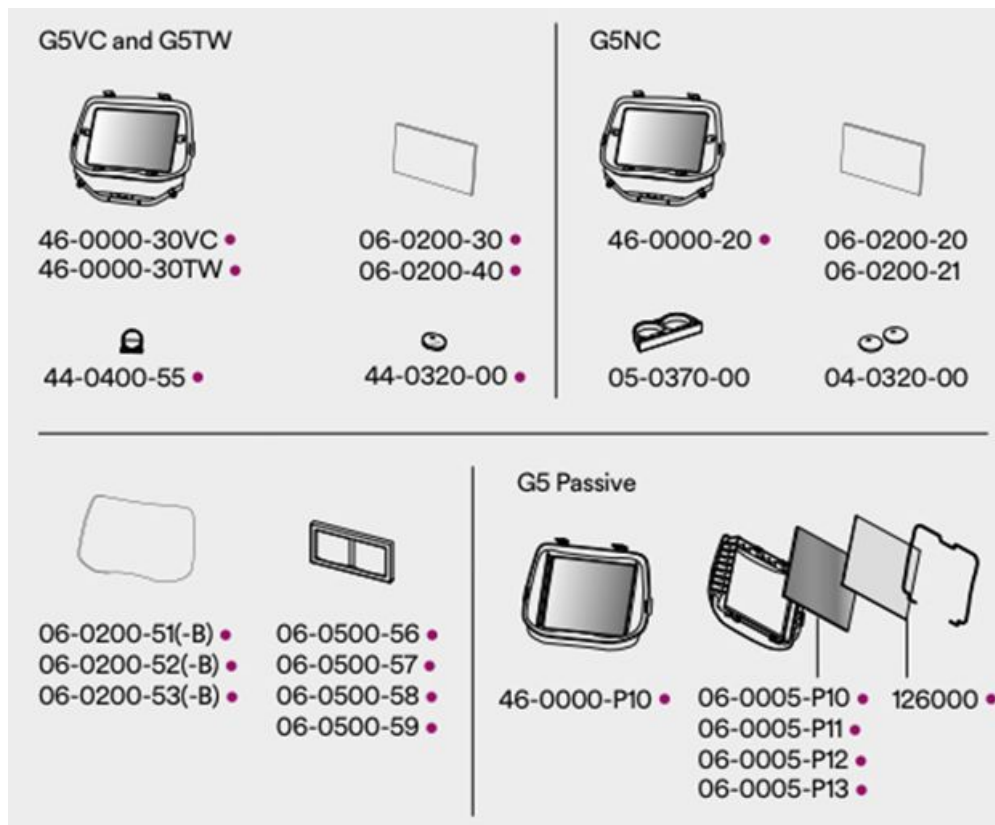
Pièces de rechange pour le filtre pour le soudage
